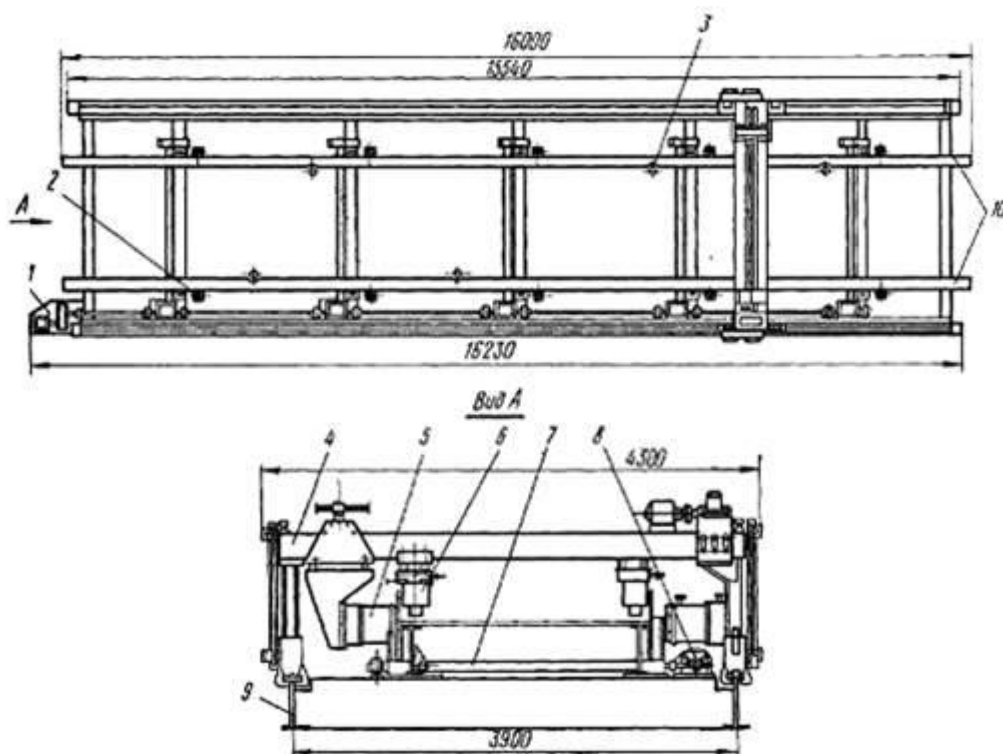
Стенд для сборки двутавровых балок с передвижным порталом: 1 - сварная рама, перемещающаяся на колесах - 6; 2 - распределительные краны сжатого воздуха; 3, 4 - горизонтальный и вертикальный пневмоприжимы захватов соответственно; 7 - механизм передвижения.
